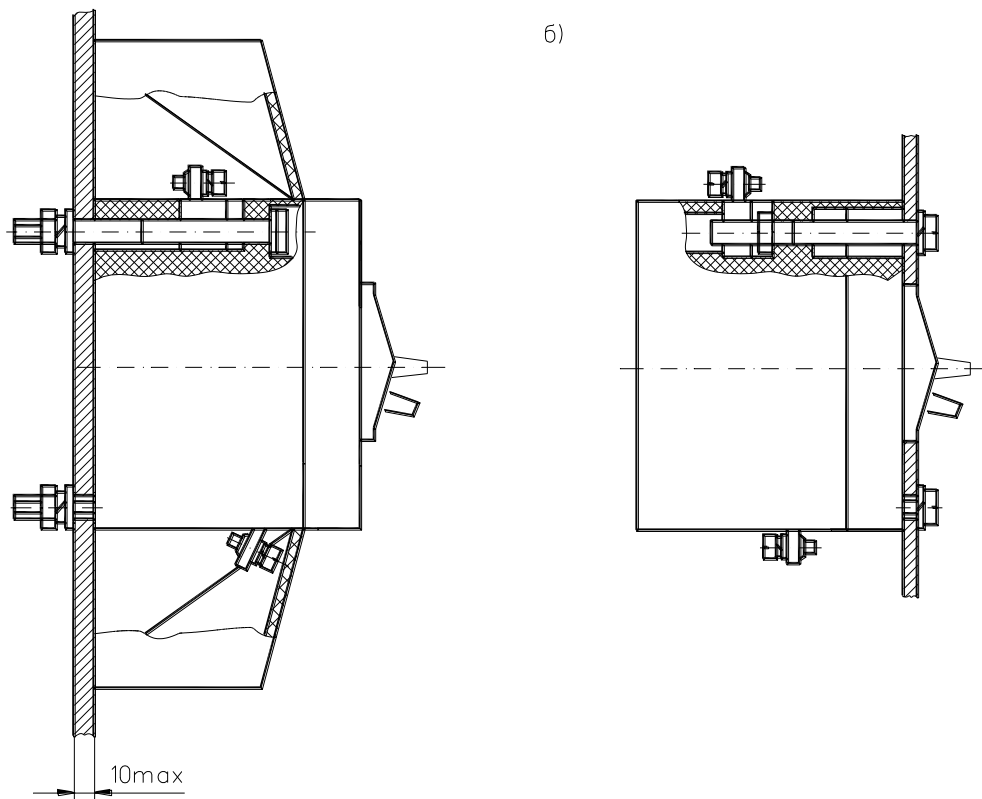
Крепление выключателя в пластмассовой оболочке:
